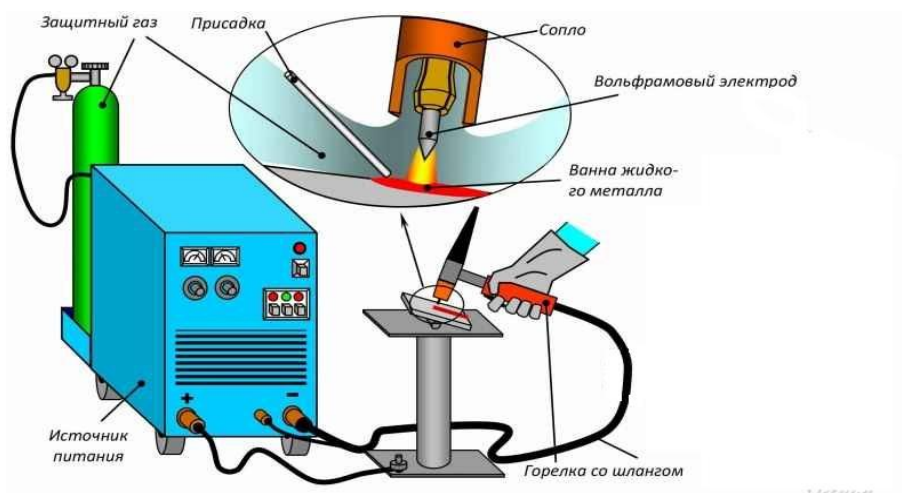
Схема ручной аргодуговой сварки
